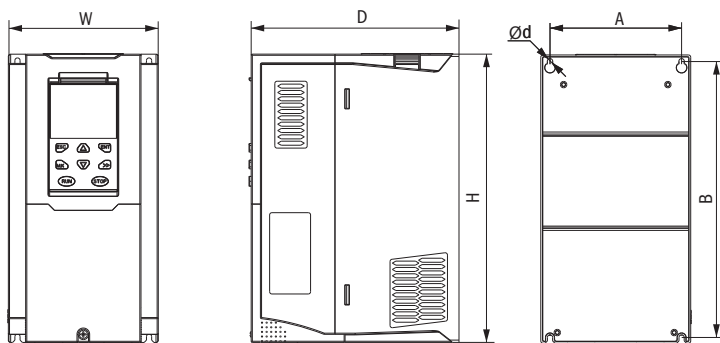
Габаритные и установочные размеры габаритов 1+3 (0,75÷15 кВт)
